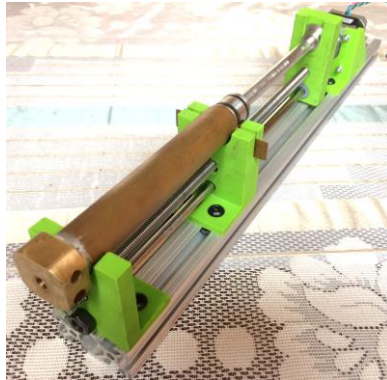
Ensamble del cilindro y émbolo con la estructura de soporte.
